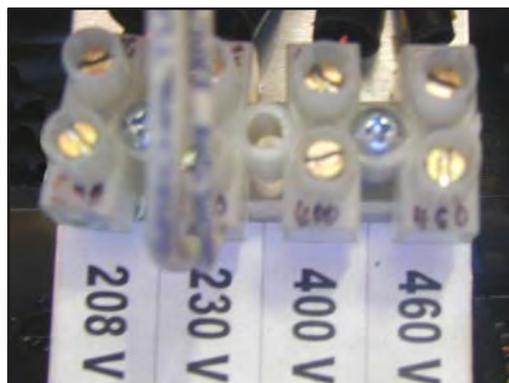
Klemmbrett Schweißtrafo VST 2500 CSA
